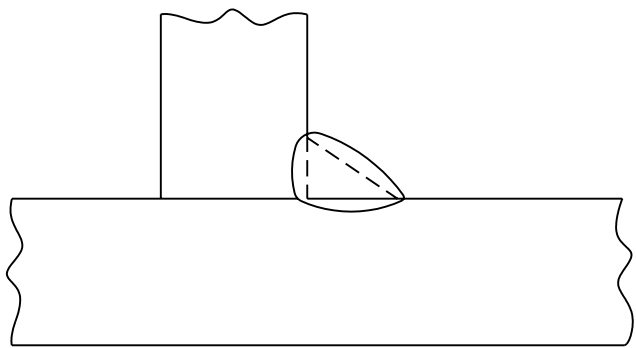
SOLDA EM ÂNGULO ASSIMÉTRICA
